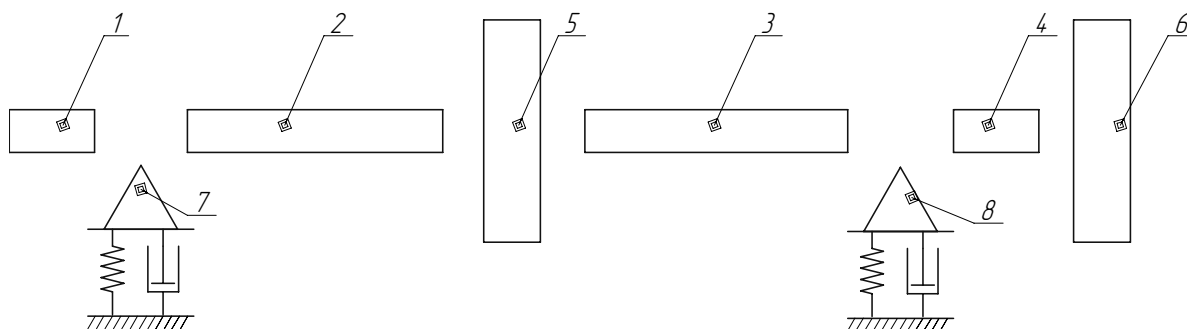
Расчетная схема шпиндельного узла с приспособлением, где 1, 2, 3, 4 –участки шпиндельного узла; 5 – зубчатое колесо, через которое передается вращение на шпиндель; 6 – приспособление; 7, 8 – подшипниковые опоры
